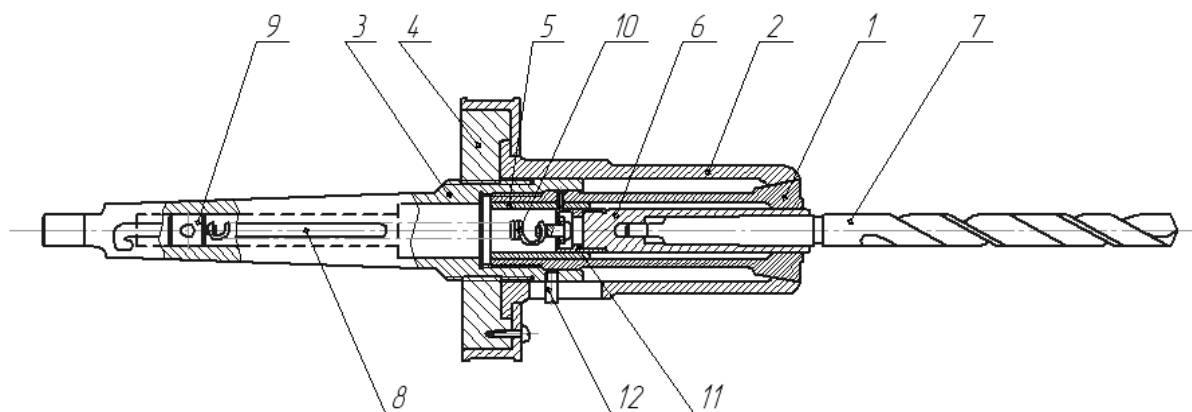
Устройство для отвода сверла. 1 – внутренняя цанга, 2 – внешняя цанга, 3 – корпус, 4 – гайка, 5 – подпружиненный элемент, 6 – направляющая втулка, 7 – сверло, 8 – направляющий паз, 9 – ползун, 10 – пружина, 11 – сухарь, 12 – стопорный винт
